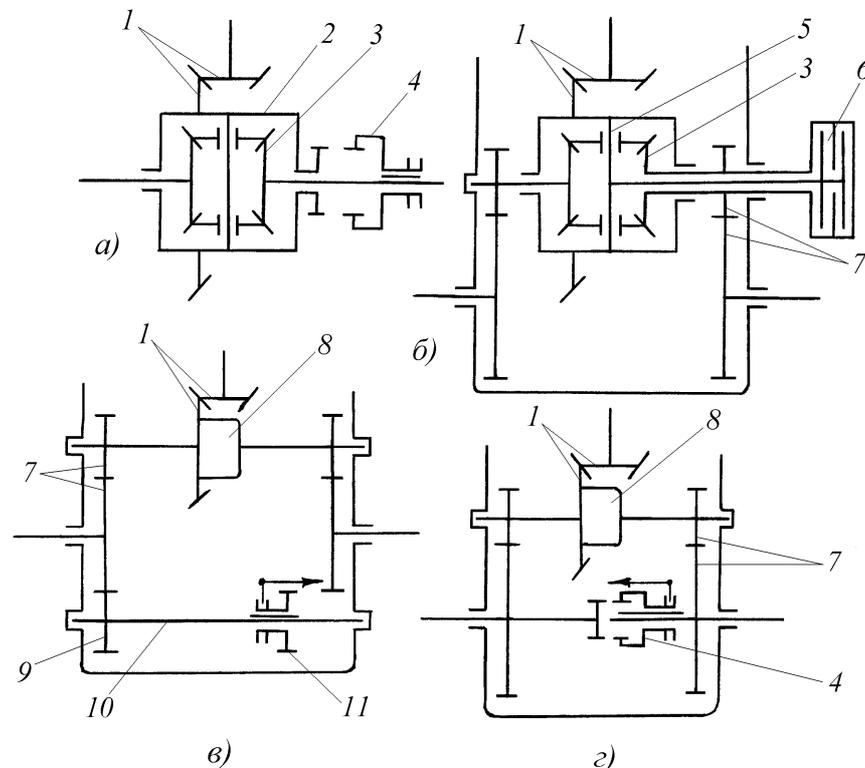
Способы блокировки межколесного дифференциала: 1 – центральная передача; 2 – корпус дифференциала; 3 – полуосевая шестерня; 4 – зубчатая муфта; 5 – ось вращения сателлитов; 6 – блокировочное фрикционное сцепление; 7 – конечная передача; 8 – дифференциал; 9 – шестерня привода блокировочного валика; 10 – блокировочный валик; 11 – блокировочная шестерня - каретка
